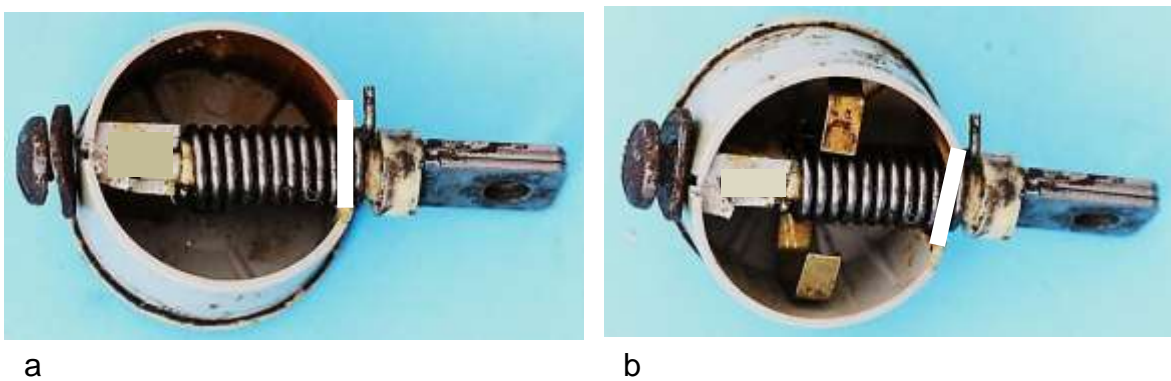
Kunststoffboden mit Drehbolzen und Druckfeder: a) Ohne Kontaktfeder, b) Mit Kontaktfeder
